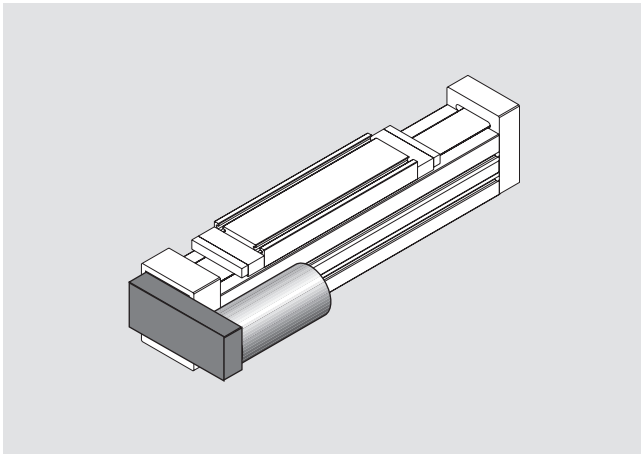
Spindeltrieb mit seitlichem Motoranbau links (Montagezustand 05)
